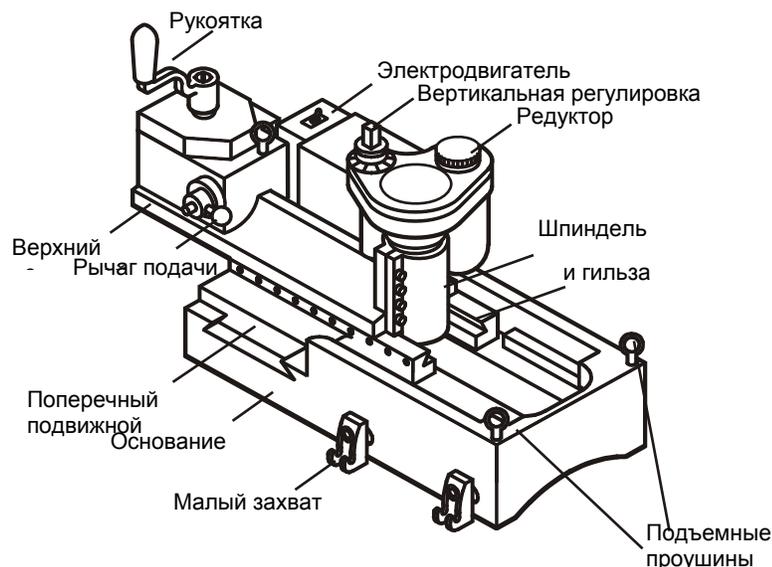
Станок для фрезерования шпоночного паза KM4000 с боковым сдвигом
